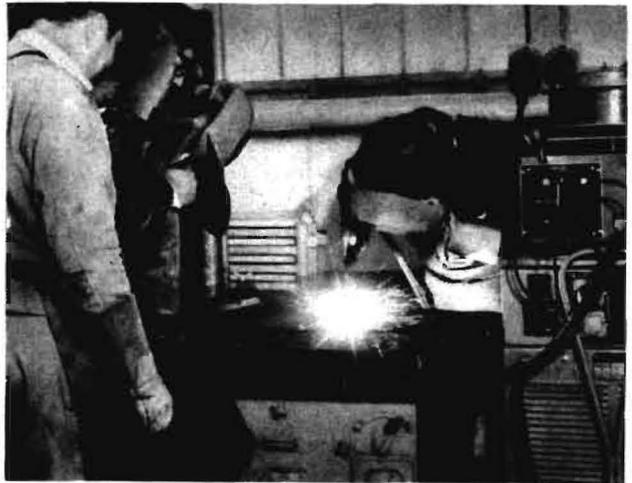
Das SG-CO₂-Schweißen wird geübt
